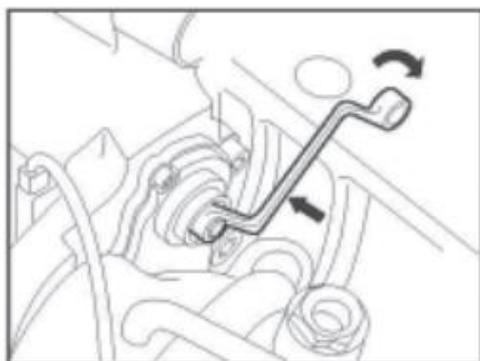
Проверка работы механизма автоматической регулировки зазора
